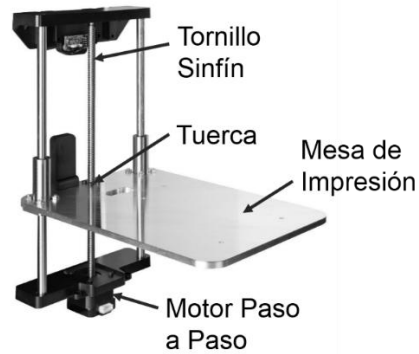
Sistema ampliamente utilizado para mover la mesa de impresión del extrusor en impresoras que utilizan el método FDM. Este mecanismo se compone de un tornillo sinfín acoplado a un motor paso a paso, el cual enrosca en una tuerca acoplada a la mesa donde se deposita el material.
